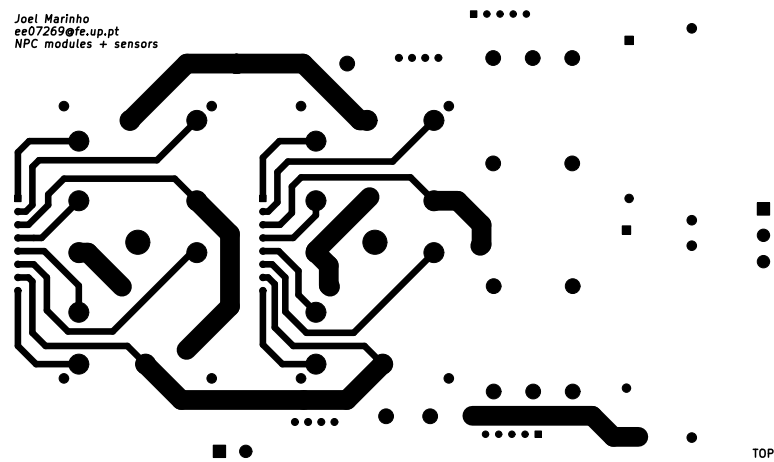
Footprint* da PCB dos módulos + sensores (*top layer*).
